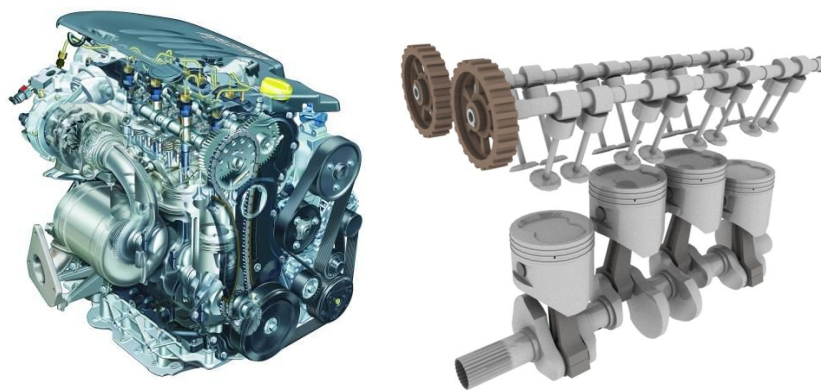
Pistón, biela, cigüeñal de un motor de C.I.
